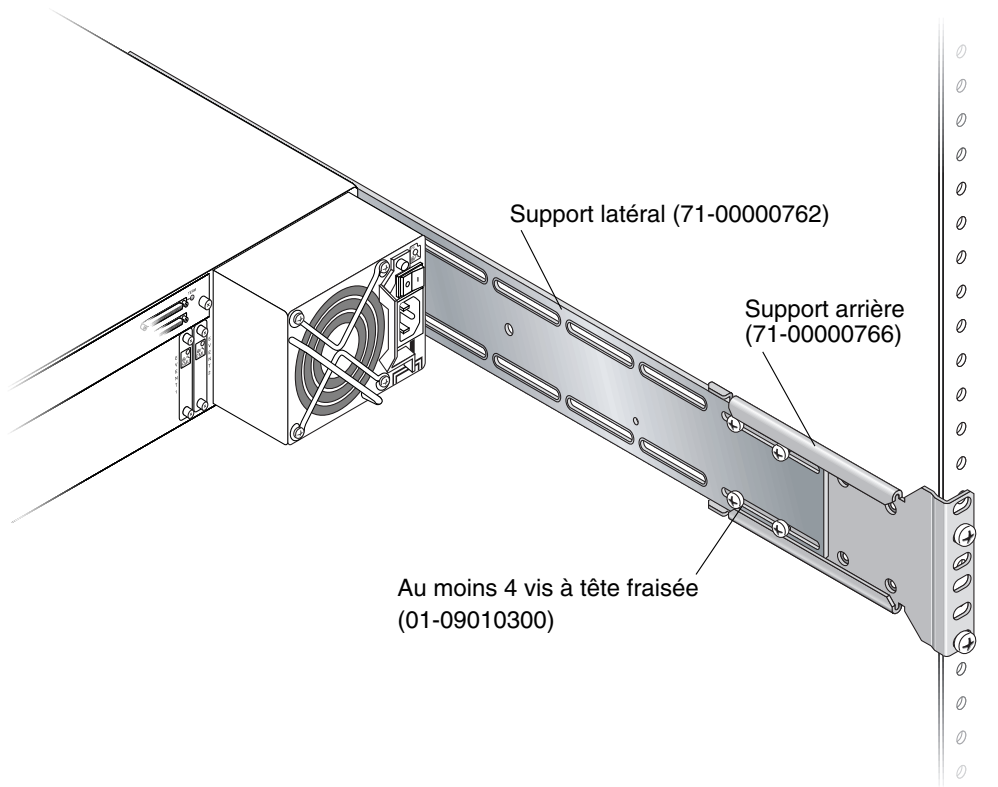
Exemple de montage de supports arrière et latéraux
